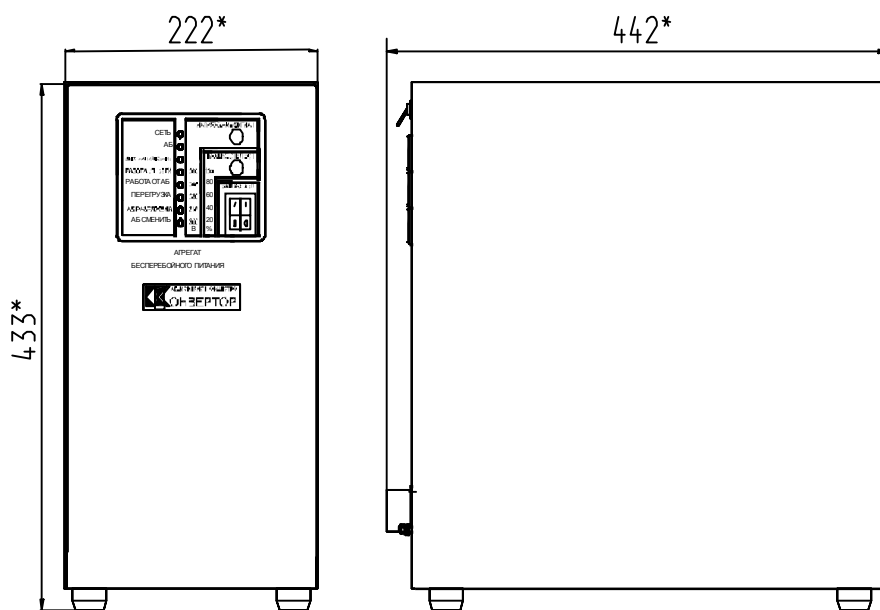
Габаритный чертеж АБП-ООПТ-4.
